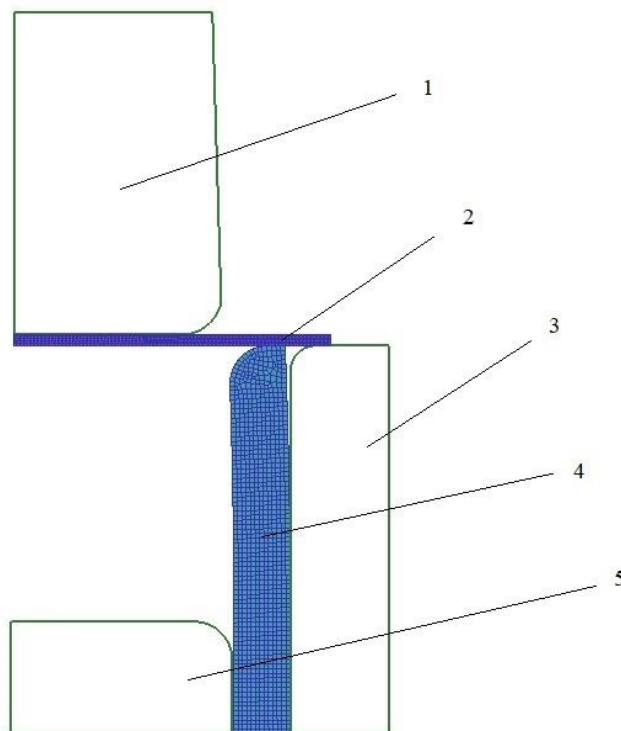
Конечно-элементная модель процесса двухугловой гибки с использованием упругих планок: 1 – пуансон, 2 - заготовка, 3 - матрица, 4 – упругая планка, 5 - выталкиватель
